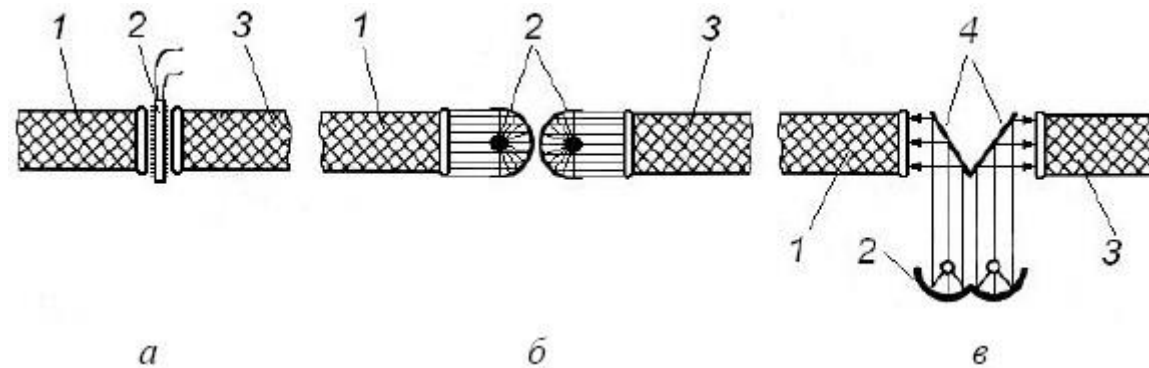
Схемы сварки световым излучением встык: 1,3 - свариваемые материалы; 2 – нагреватели; 4 - зеркальные отражатели
